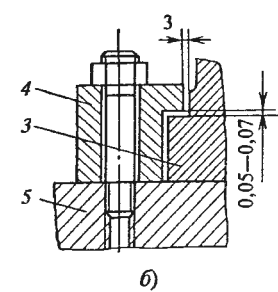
Крепление корпуса подшипника к фундаментной раме:
